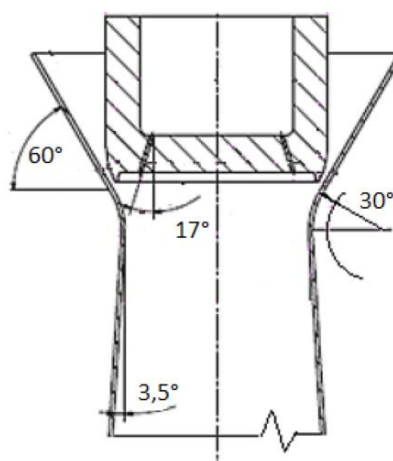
Odtržení proudu na bočních stěnách [32], [33]
